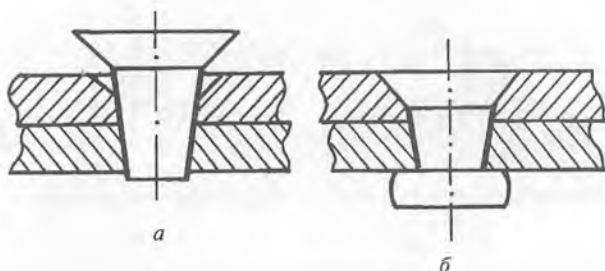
Соединение конусными заклепками: а — конструкция заклепки; б — установленная заклепка
